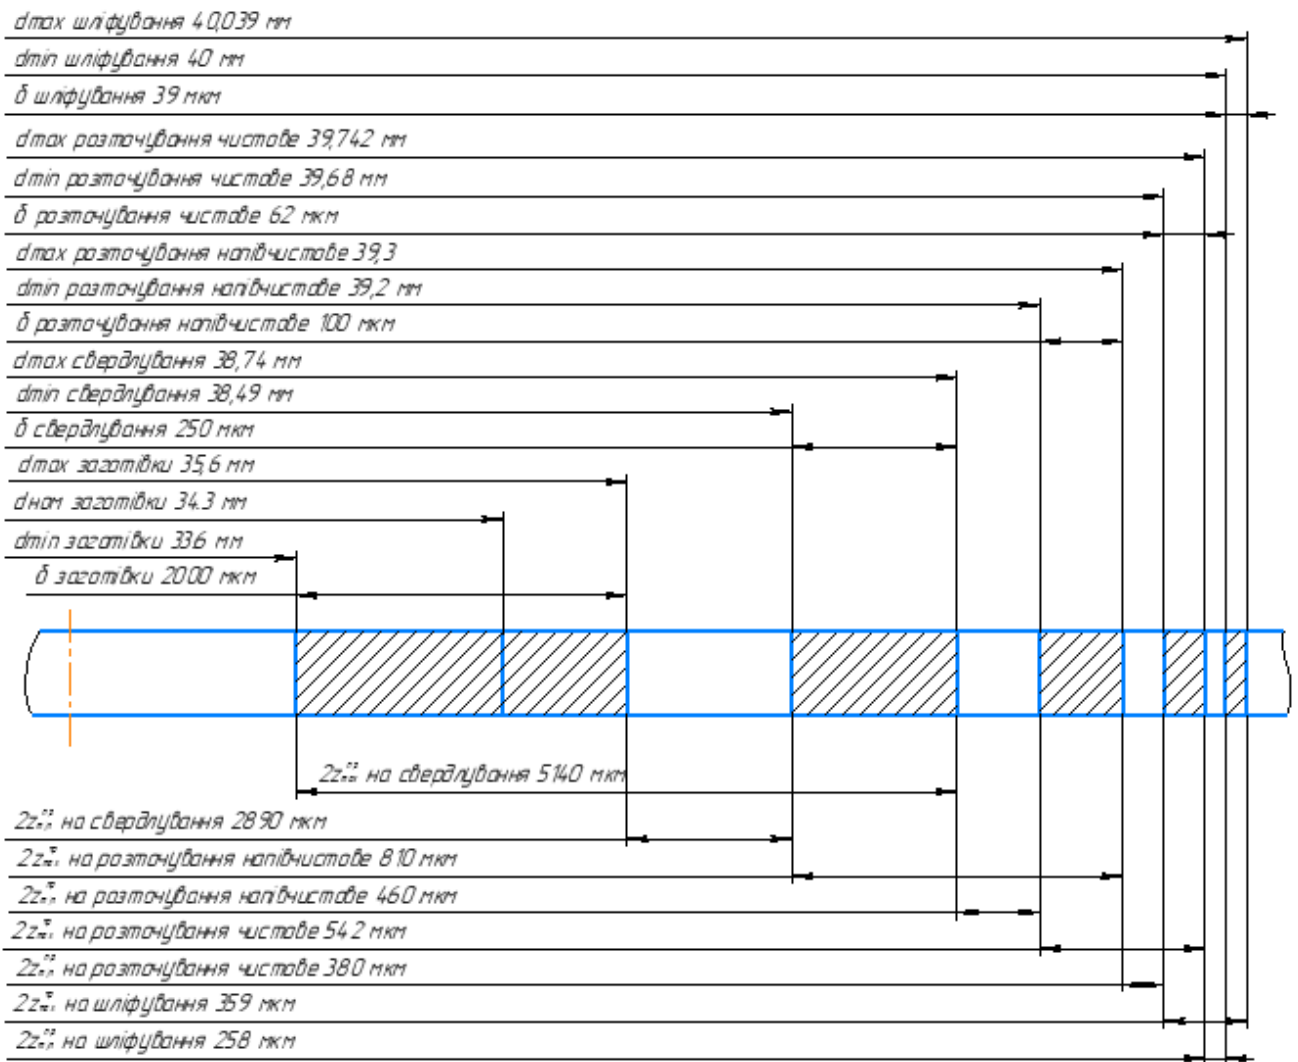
Схема розташування припусків та допусків
